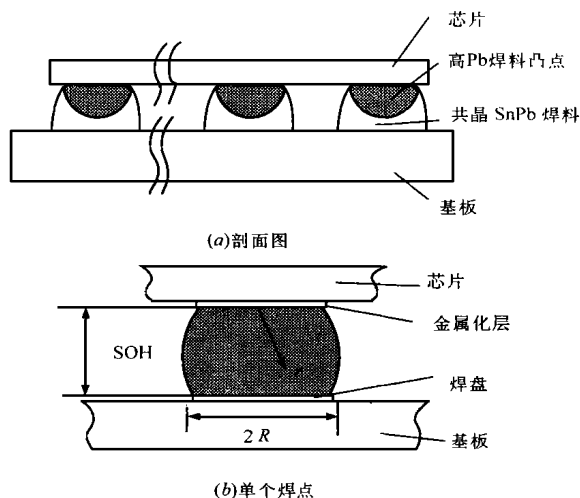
倒装焊复合 SnPb 焊点结构示意图(SOH (solder joint height) 为焊点高度; r 为焊料凸点半径; R 为焊盘半径)
